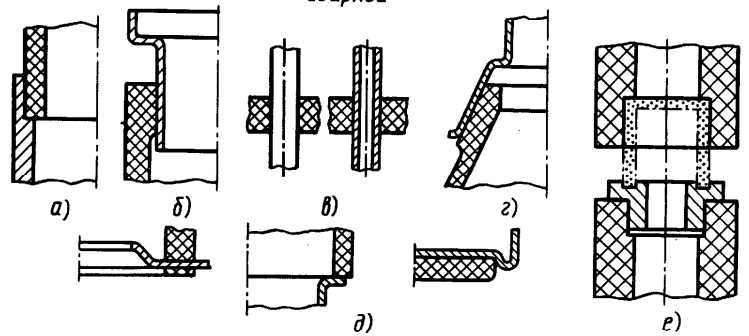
Конструкции соединений керамики с металлами диффузионной сваркой: а - цилиндрические охватывающие; б и в - цилиндрические охватываемые; г - коническое охватывающее; д - торцовые; е - деталь в сборе
